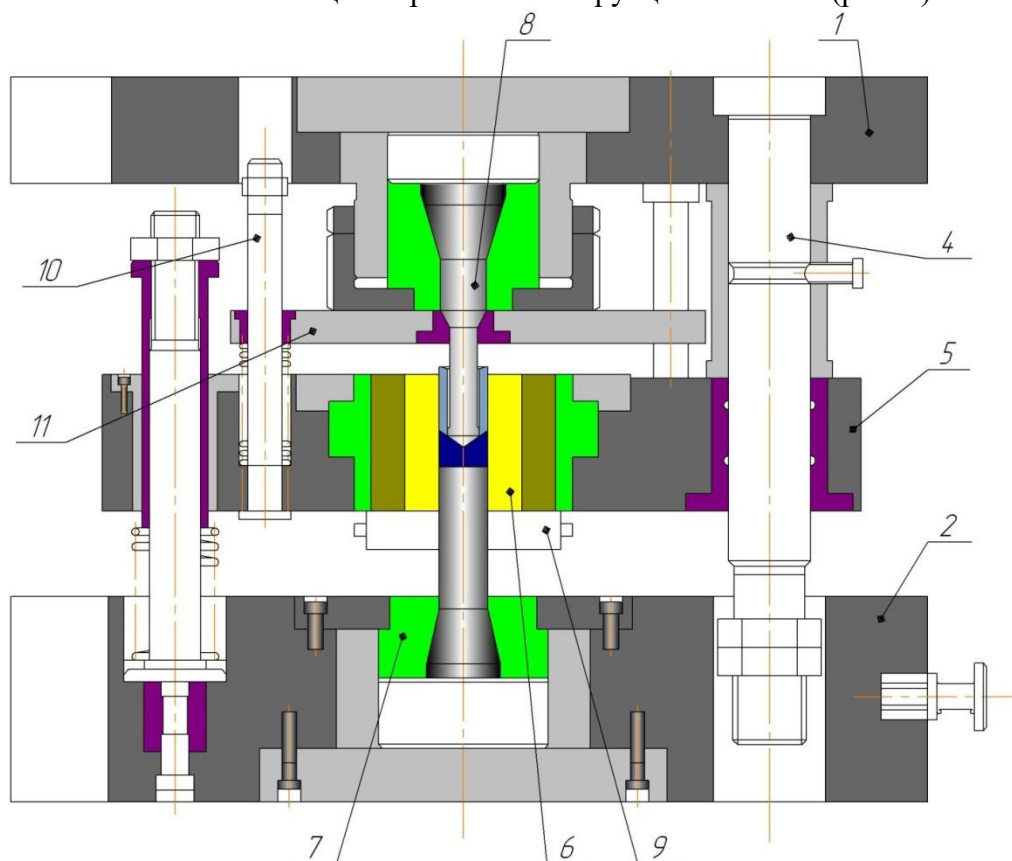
Штамп для сквозной прошивки деталей типа втулок
